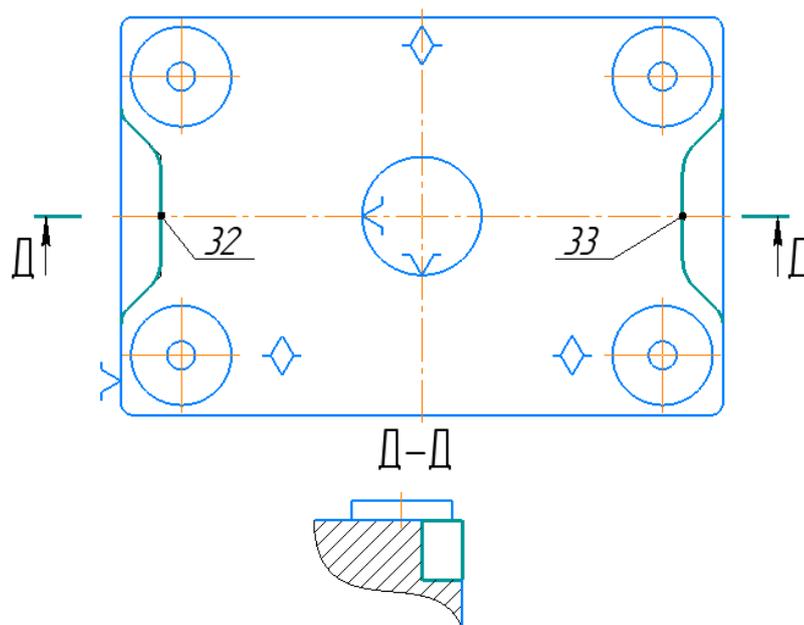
Эскиз фрезерной с ЧПУ операции
